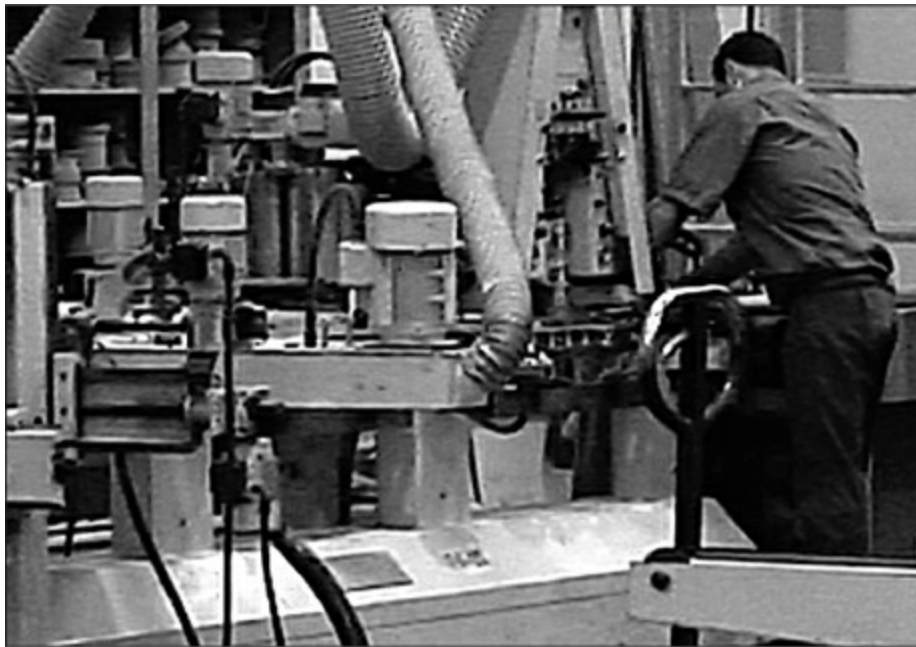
Equipamiento y otros elementos de un puesto de trabajo.
